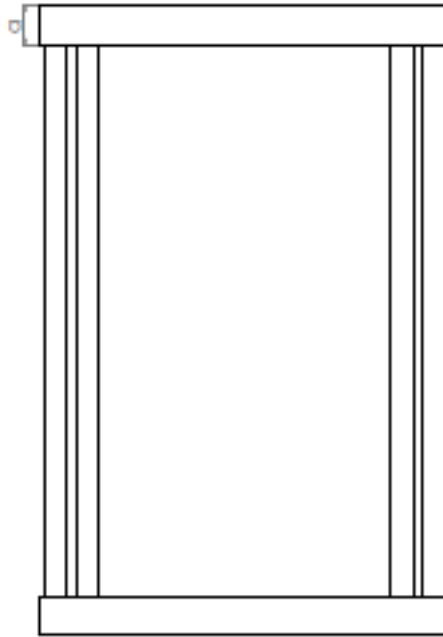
12 Dimensionamiento para la soldadura [Autor]
